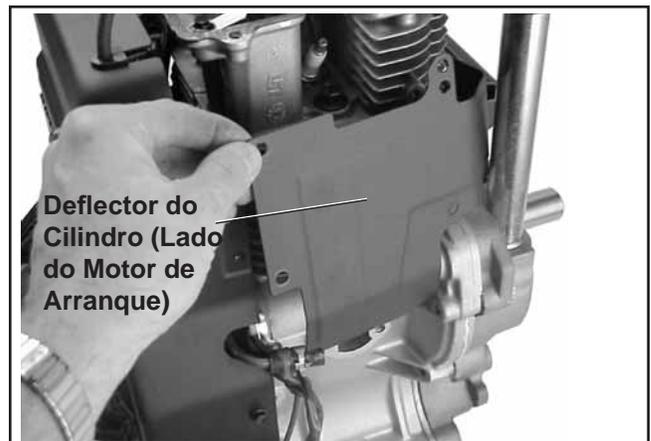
Retirar o Deflector do Cilindro do Lado do Motor de Arranque
